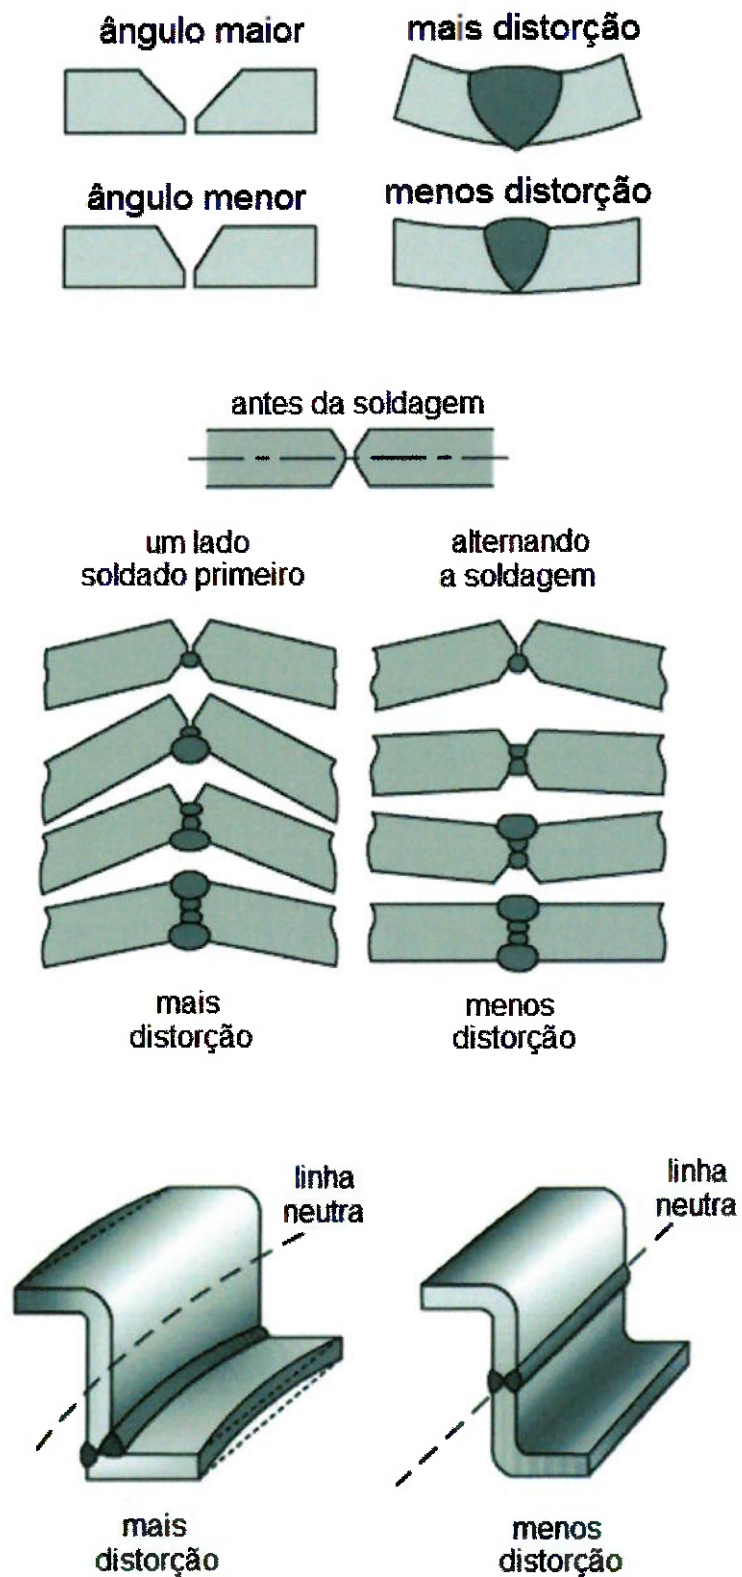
Algumas técnicas para redução de distorções por soldagem [7, adaptado]
